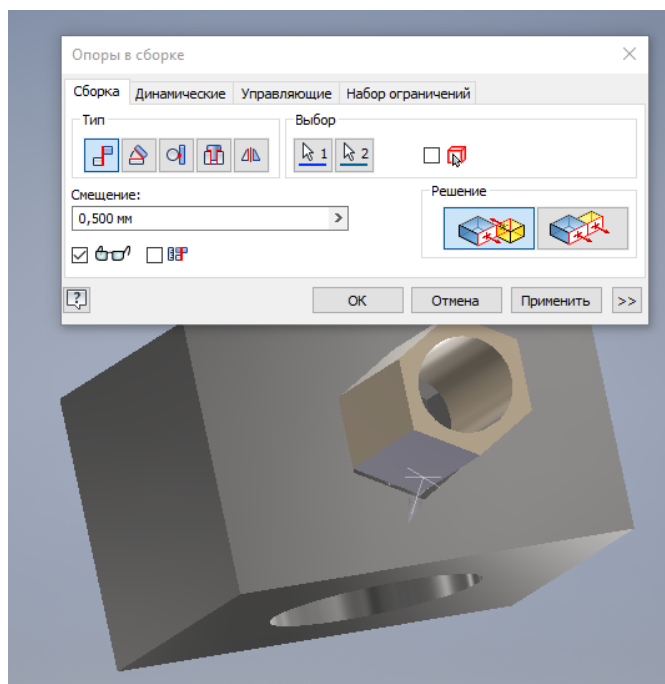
Совмещение боковой грани патрубка и призматического отверстия корпуса со смещением 0,5 мм
